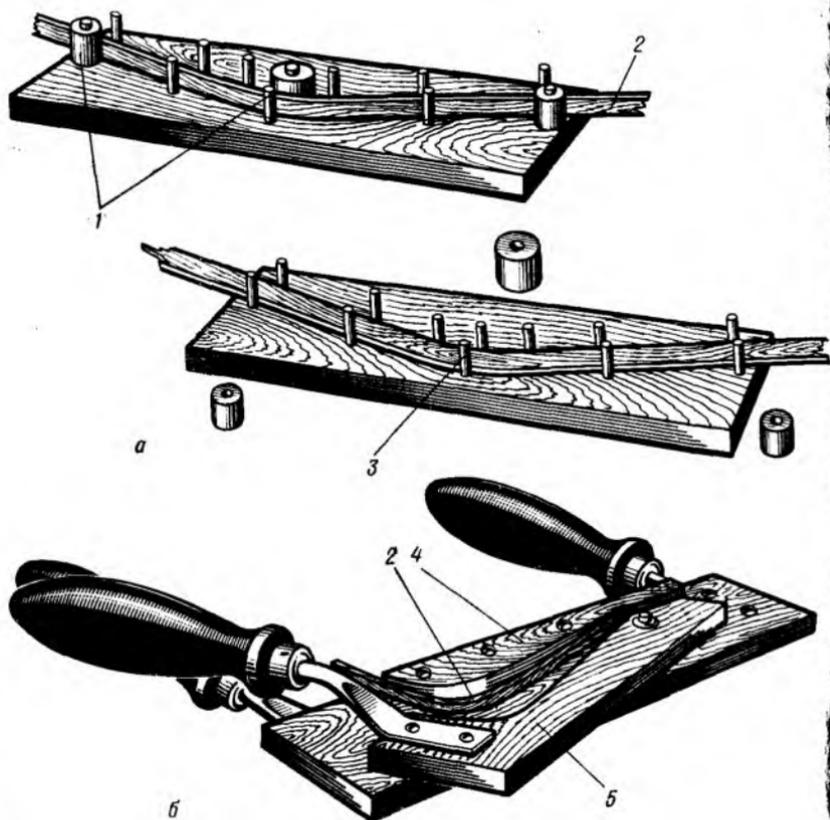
Приспособления для изгибания кромок (а) и нервюр (б):
